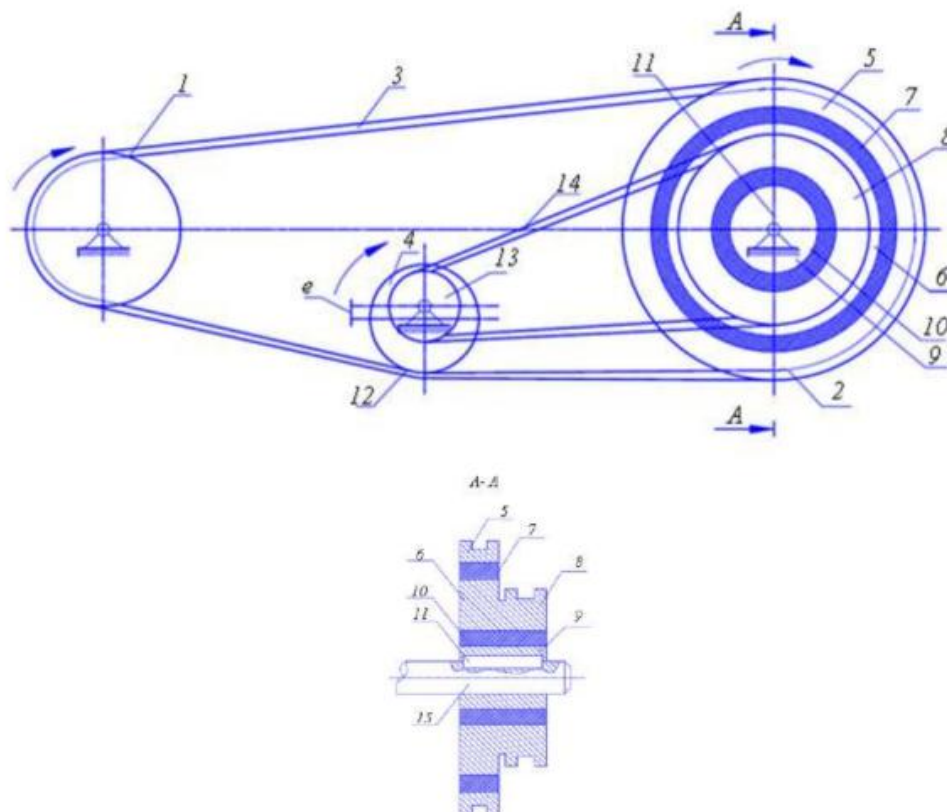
Схема ременная передача, стабилизирующая движение ведущего шкива
